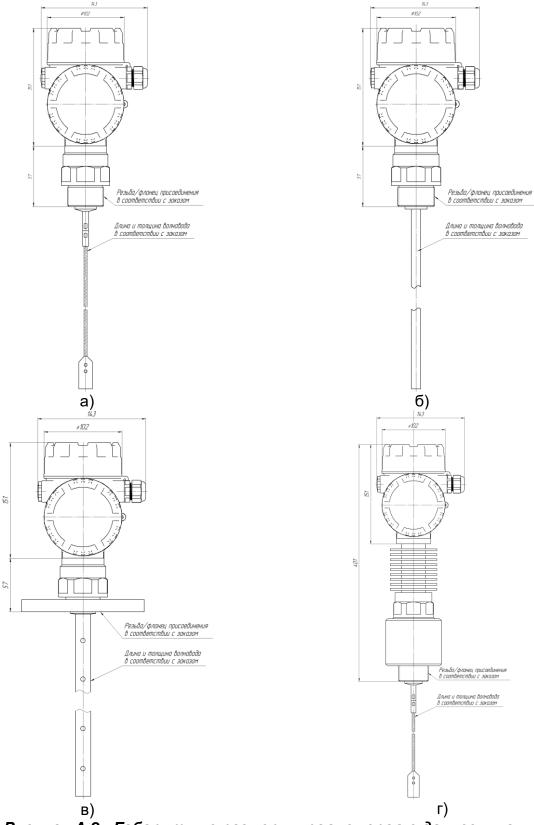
Габаритные размеры уровнемеров с двухсекционным исполнением корпуса
